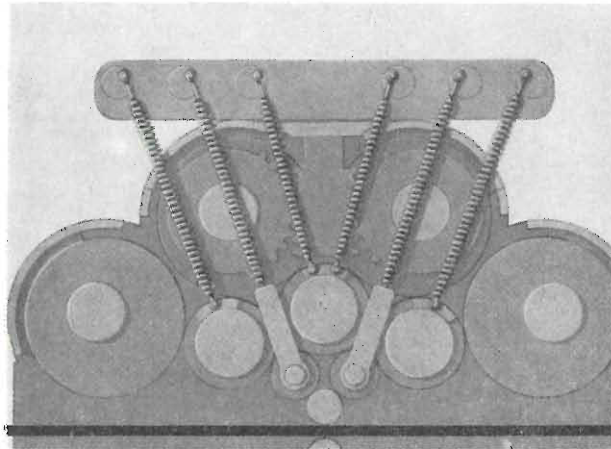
Spostamento dei cilindri di lavoro mediante rotazione eccentrica degli elementi di spallamento.
